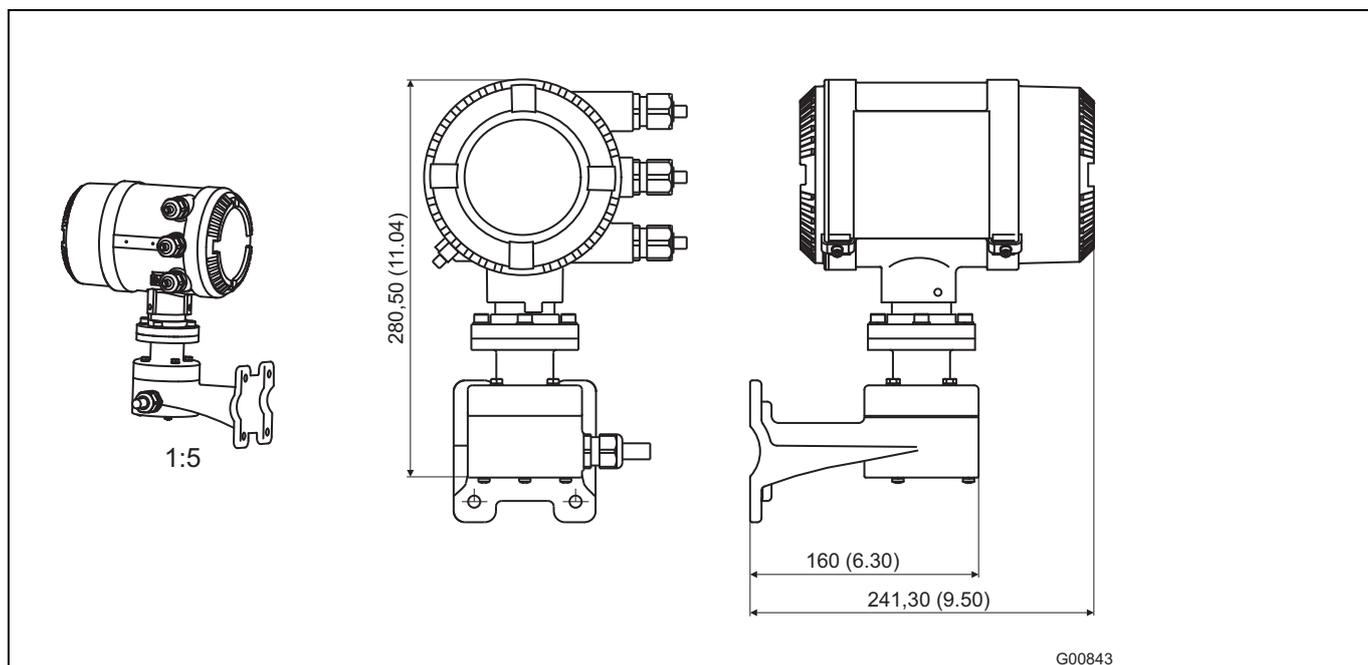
Dimensiones de la carcasa del transmisor ME26/27/28
